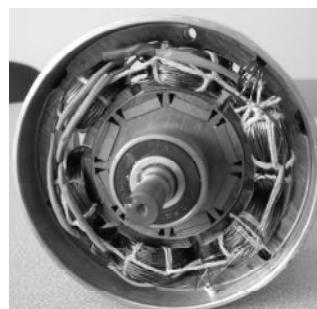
Макетный образец ВД с внутренними магнитами (снят передний подшипниковый щит)
